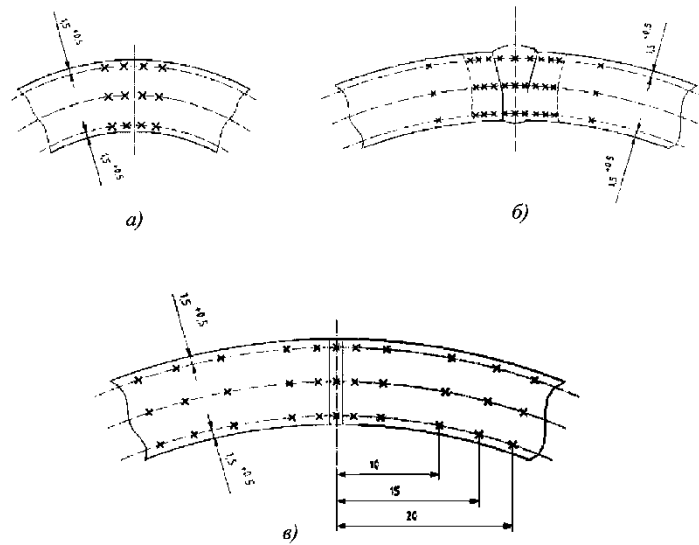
Розташування точок вимірів твердості: *a* — безшовний елемент; *б* — дугове зварювання; *в* — високочастотне зварювання
